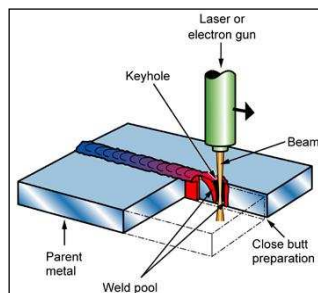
INTEGRACIÓN POR SOLDADURA: SOLDADURA LASER
